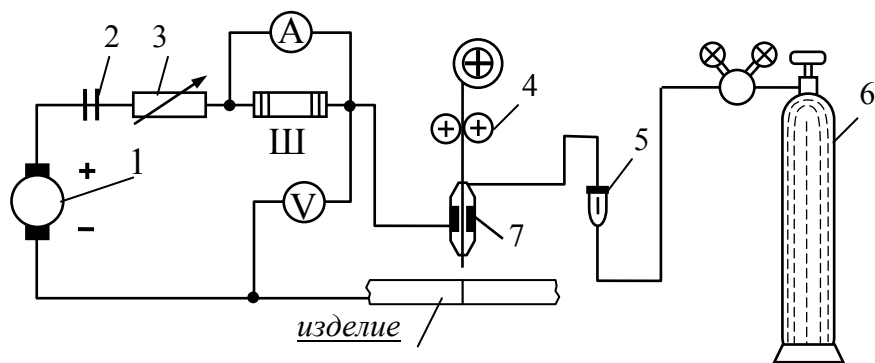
Схема сварочного поста для механизированной дуговой сварки в защитных газах
